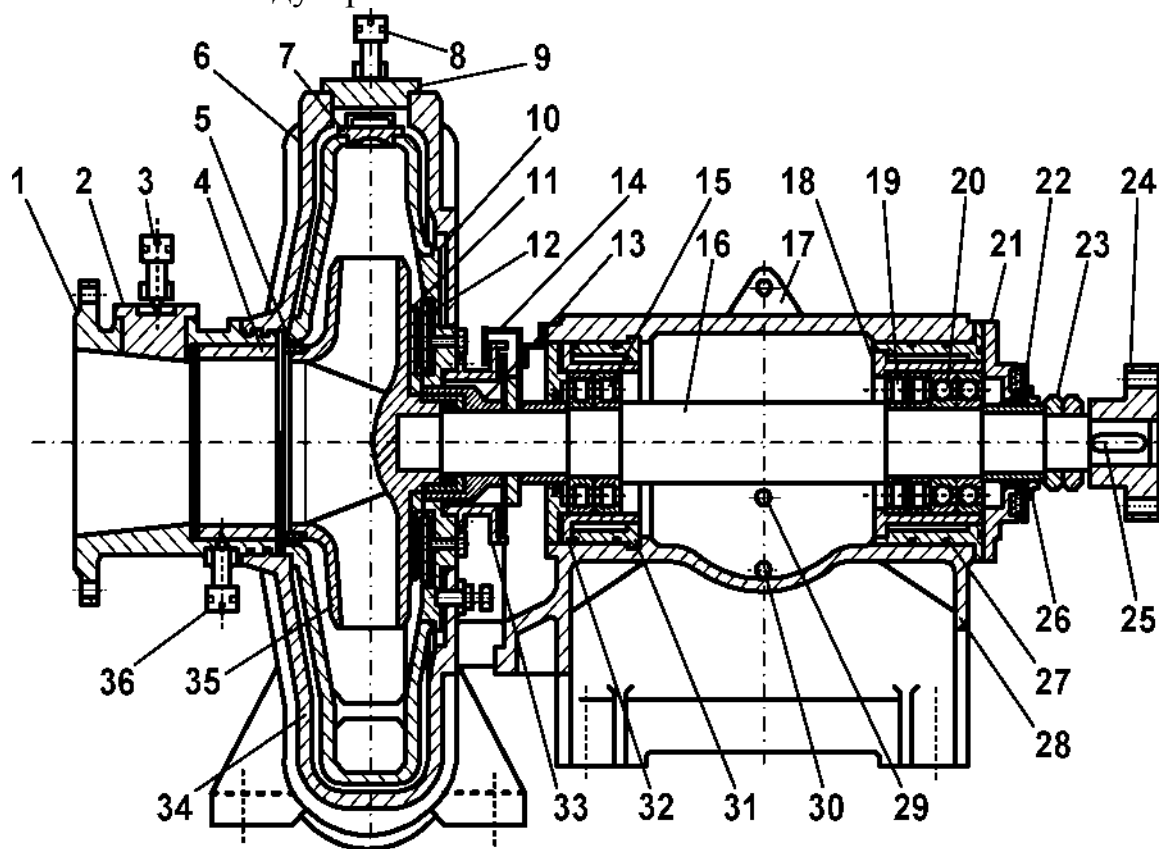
Конструкция углесоса 14У-7: 1 - всасывающий патрубок; 2, 7 и 9 - заглушки патрубка, протектора и корпуса; 3, 8 и 36 - клапаны продувки; 4 - защитная втулка; 5 - уплотнительная втулка; 6 - корпус; 10 - фланец внутренний; 11 и 12 - бронедиски; 13 - дистанционная втулка; 14 - торцевое уплотнение; 15 и 19 - радиальные подшипники; 16 - вал; 17 - рымбол; 18 и 31 - стакан; 20 - радиально-упорные подшипники; 21 - фланец подшипниковой опоры; 22 - лабиринтное уплотнение; 23 - стопорная гайка; 24 - полумуфта; 25 - шпонка; 26 - упорная втулка; 27 - кольцевое уплотнение; 28 - станина; 29 - смотровое стекло; 30 - сливная пробка; 32 -
